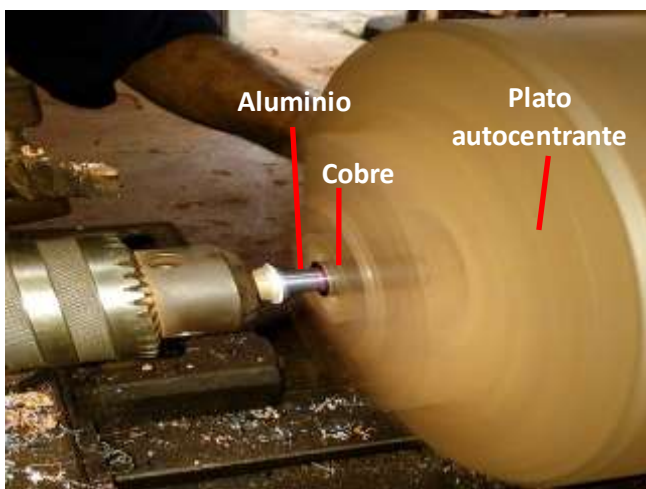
Instalación del proceso de soldadura por fricción.
